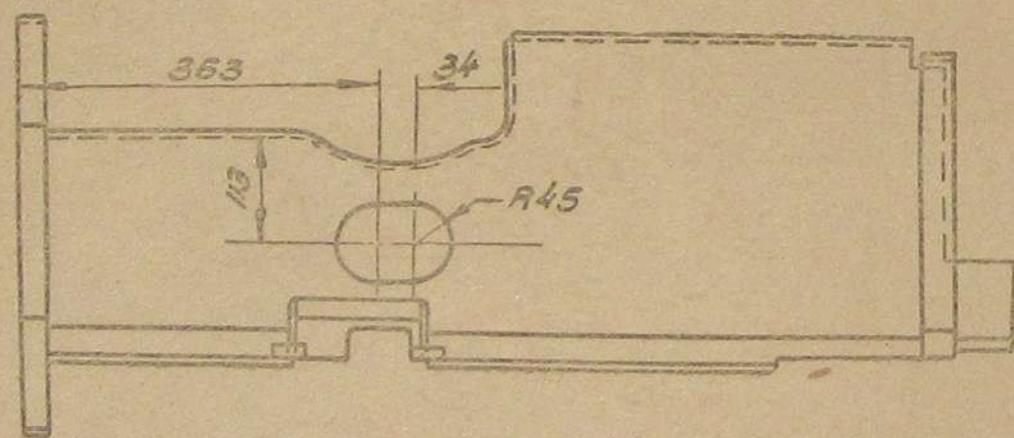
Правая боковина кожуха на мотор ЗИС-5 с изменениями для установки Г69.
